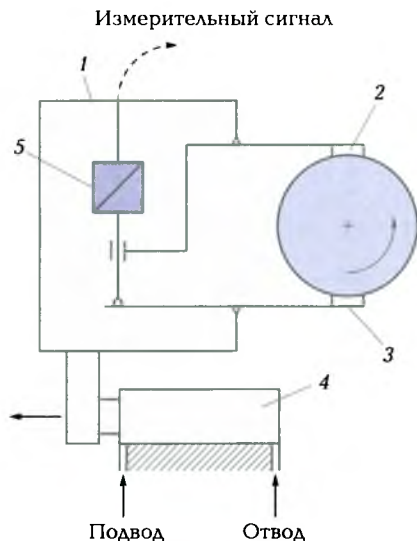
Прибор с двумя подвижными измерительными рычагами:
